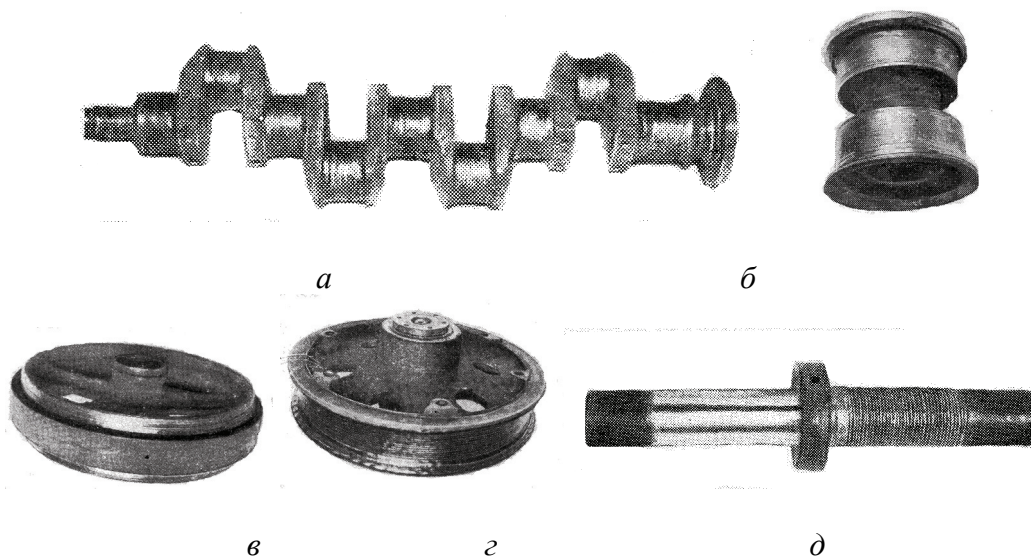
Деталі, відновлені наплавленням: а – колінчатий вал трактора ДТ-54; б – однобортний опорний каток трактора; в – натяжне колесо; г – кранове колесо; д – вісь опорного катка
